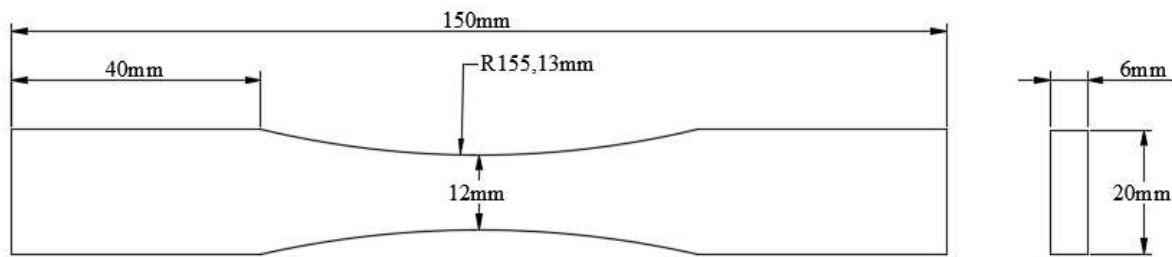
Dimensiones de la probeta para fatiga de acuerdo con la norma ASTM E466-96
